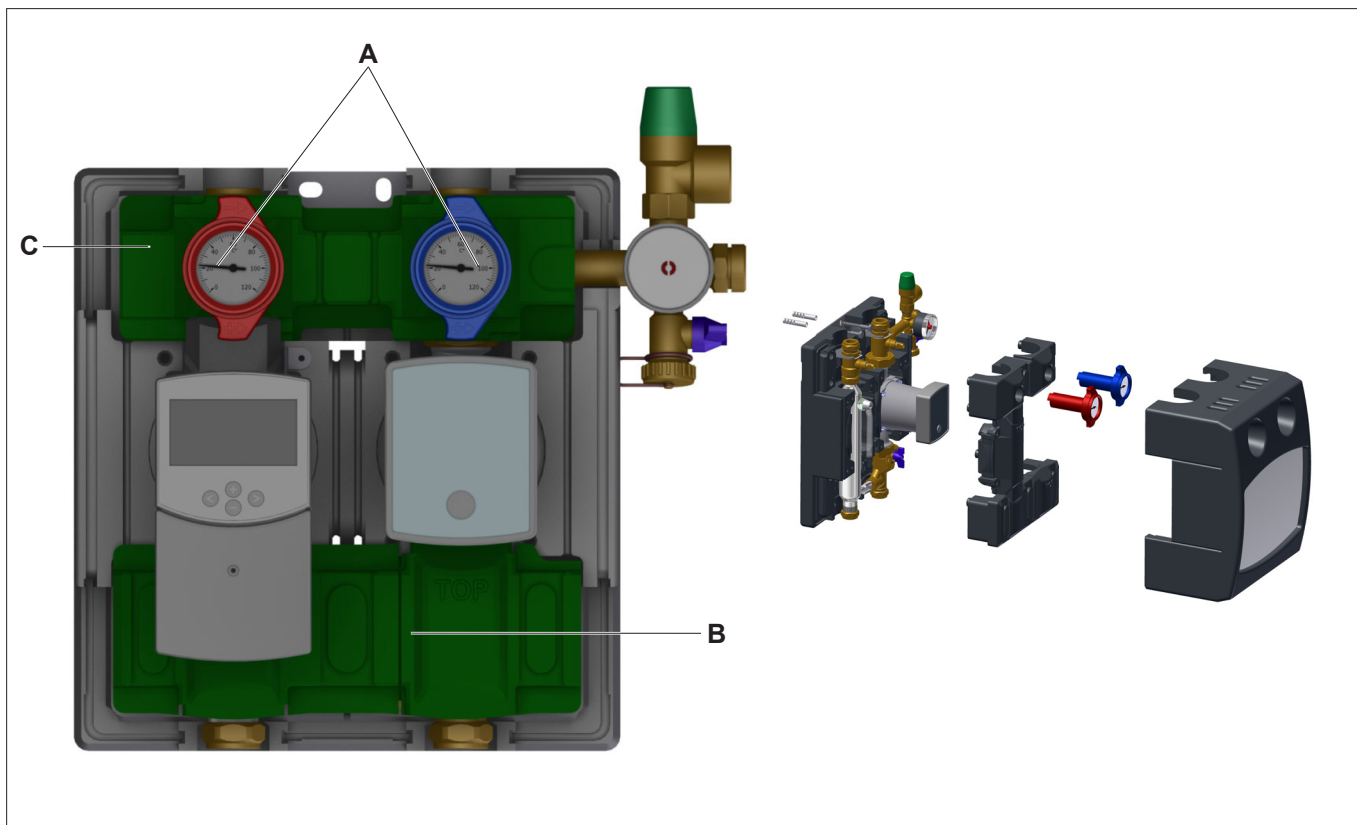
Isolierungen demontieren (dargestellt am Typ 8130 mit Entlüfterrohr und Regler)
